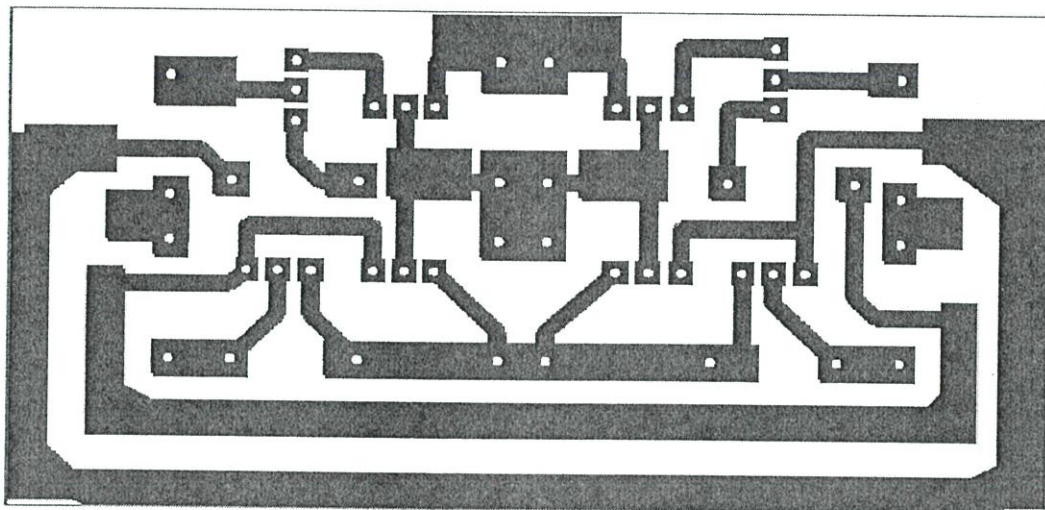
แสดงการต่อวงจร Charge Board ลงบนแผ่น PCB
